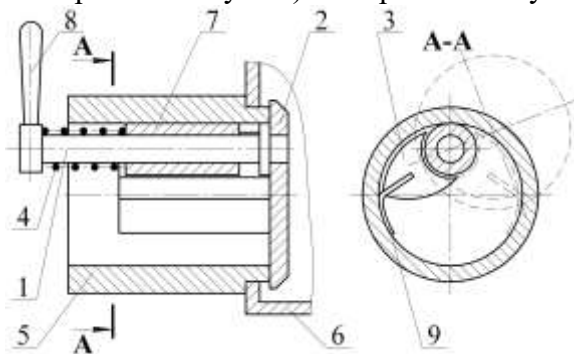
Ексцентриковий затвор: 1 – вал; 2 – запірний диск; 3 – лопать; 4 – пружина; 5 – порожниста опора; 6 – горловина бункера; 7 – втулка; 8 – ручка; 9 – еластичний елемент;
